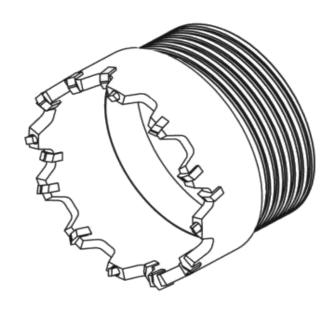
Породоразрушающий инструмент – коронка СМ3
